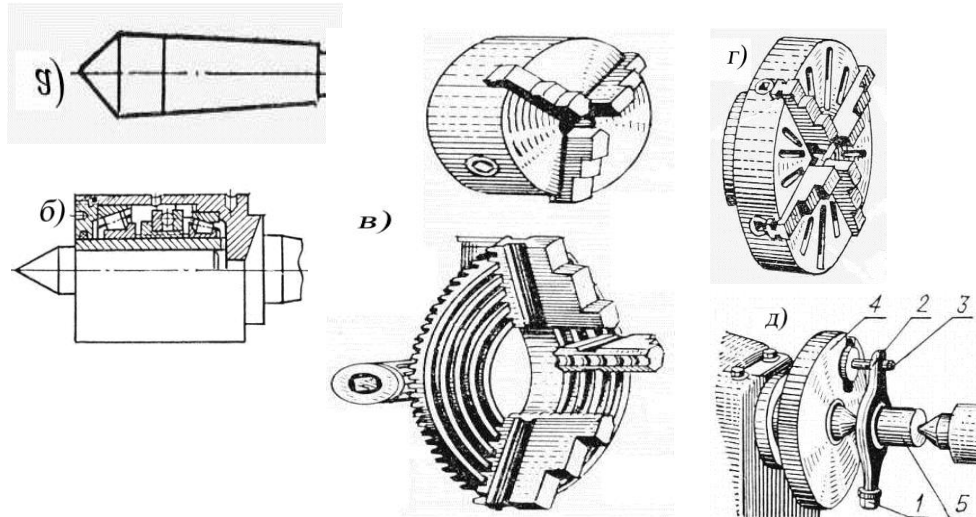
Приспособления токарного станка: а – центр неподвижный, б – центр вращающийся, в - трехкулачковый самоцентрирующийся патрон, г – четырехкулачковый патрон, д – поводковый патрон: 1 - зажимной винт, 2 - хомутик, 3 - поводок, 4 - поводковый патрон, 5 – заготовка
